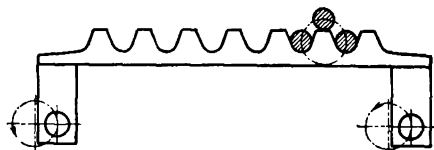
Приспособление для передачи заготовки из ручья в ручей
